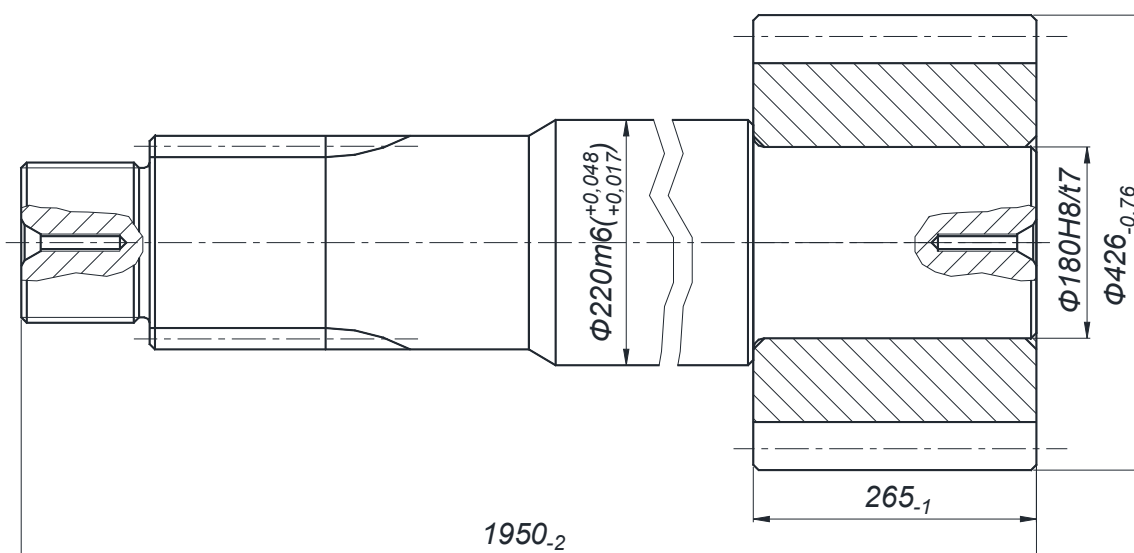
Вал шестерня экскаватора ЭКГ-8
